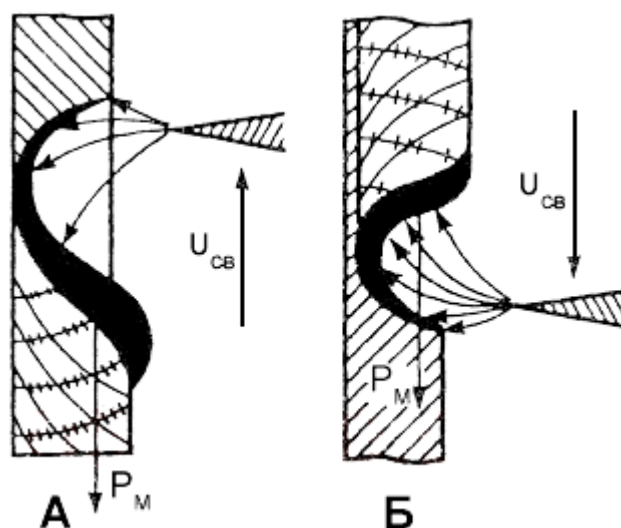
Ручная дуговая сварка швов в вертикальном положении
